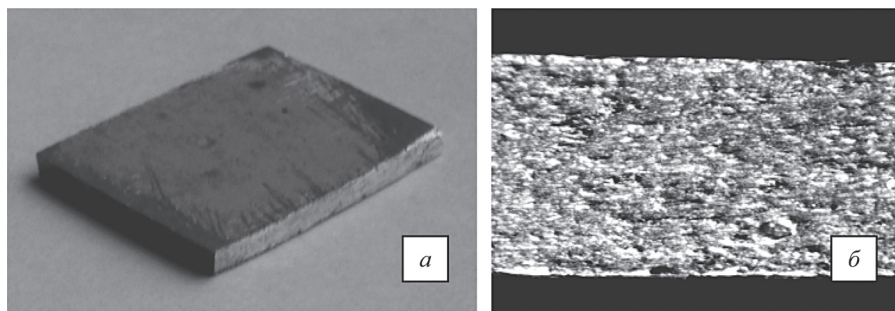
Двухслойный образец из алюминиевых пластин, соединенных сваркой давлением: *a* – внешний вид; *б* – фрагмент слоистой структуры
